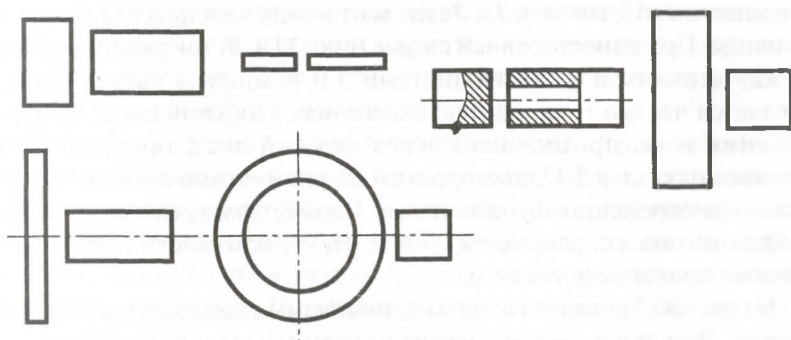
Примеры сварных соединений стыковой сварки оплавлением
